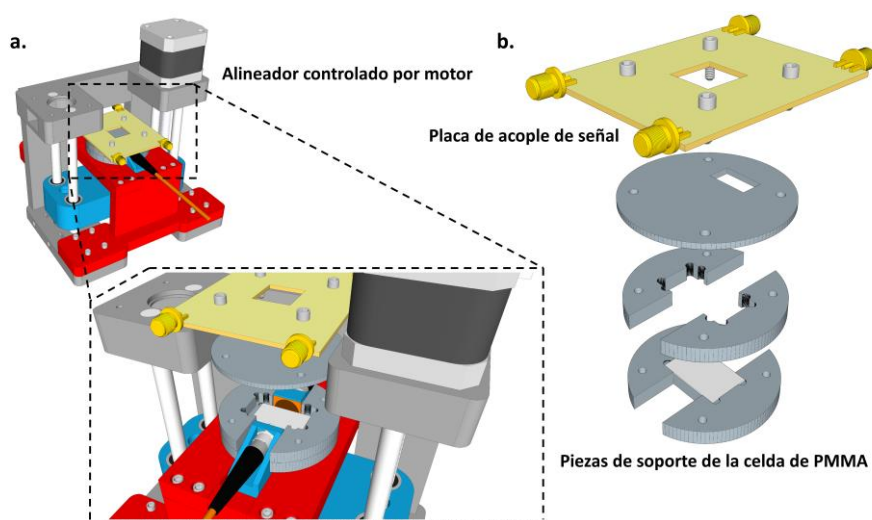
(a) Detalle del microposicionador motorizado. (b) Partes de PMMA de la celda de prueba adaptada y placa electrónica de contacto. Reproducido de [28].
